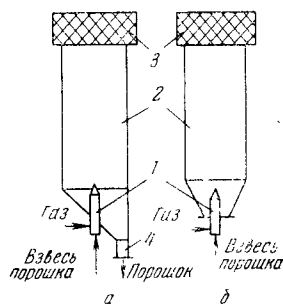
Конструкции вертикальных цилиндрических сепараторов (насадок): а — первого типа; б — второго типа; 1 — форсунка; 2 — цилиндрический корпус; 3 — фильтр; 4 — сборник крупного порошка
